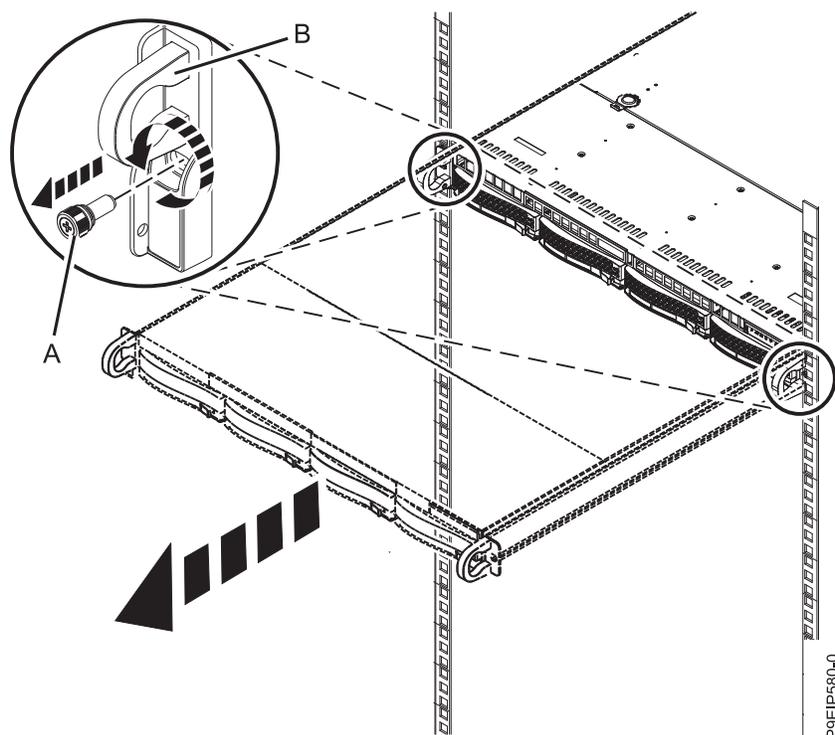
Removendo os parafusos frontais e removendo o sistema do rack
